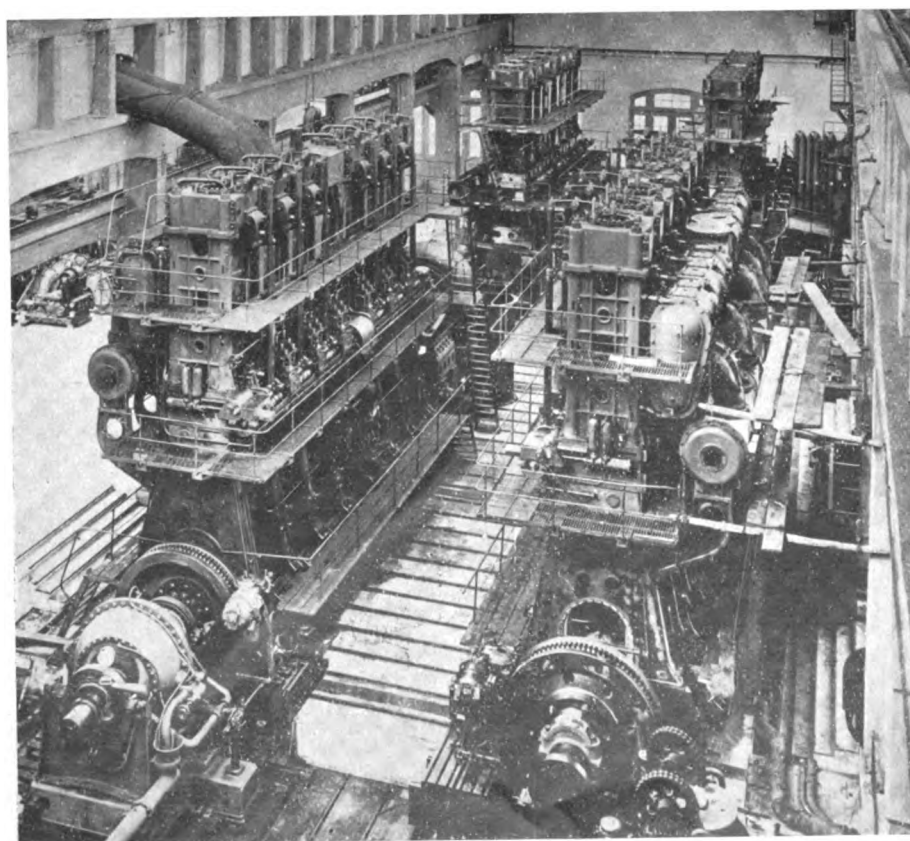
4 Hauptmotoren von je 9000 PSI auf dem Probestand
